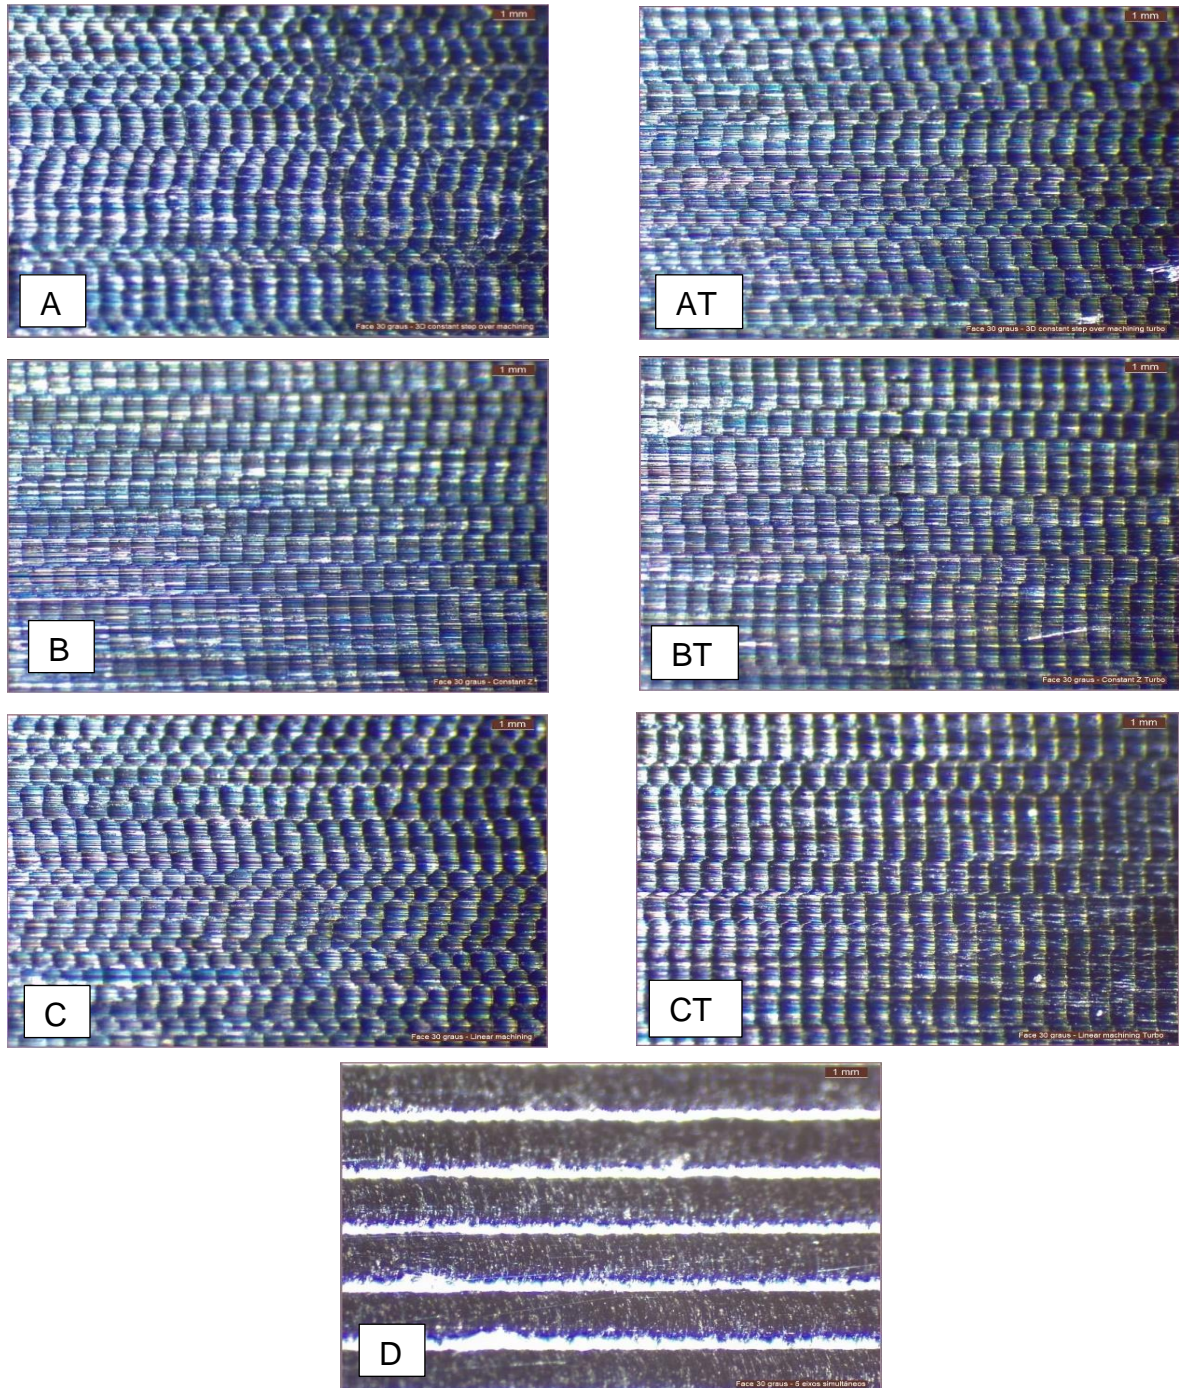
A: Estratégia de maquinagem Passagem constante 3D; AT: Estratégia de maquinagem Passagem constante 3D turbo; B: Estratégia de maquinagem Constante Z; BT: Estratégia de maquinagem Constante Z turbo; C: Estratégia de maquinagem linear; CT: Estratégia de maquinagem linear turbo; D: Estratégia de maquinagem 5 eixos simultâneos
